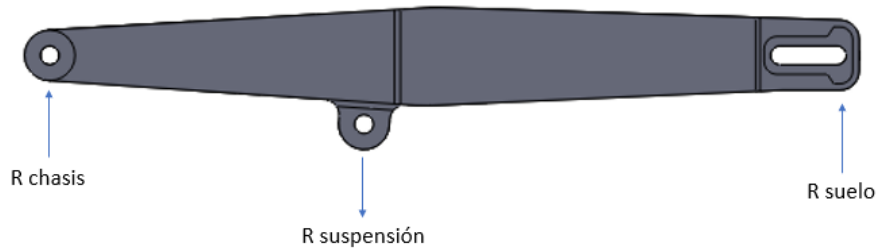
Ejemplo de basculante y las fuerzas que aplican sobre él.
